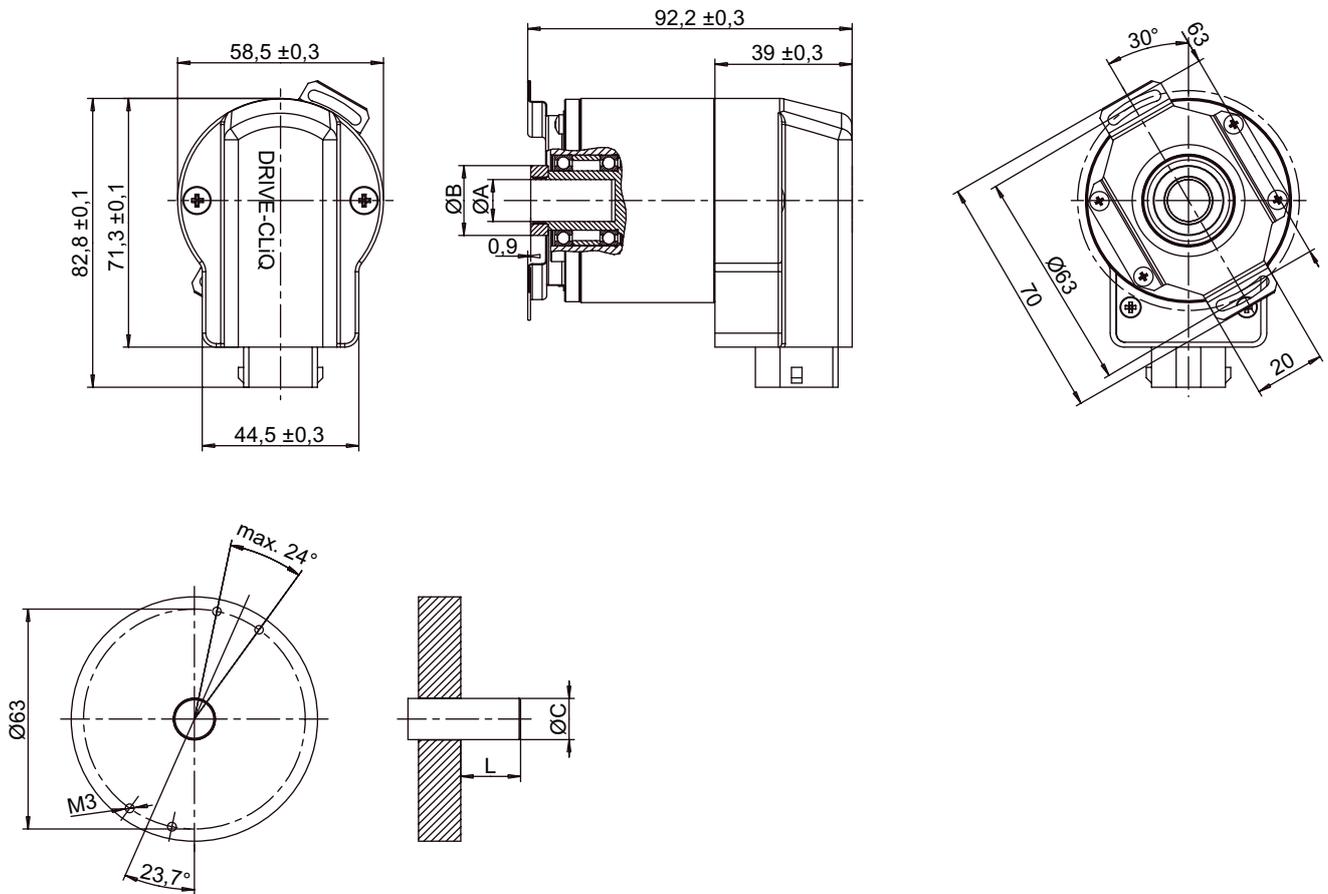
Maßzeichnung: Sack-Hohlwelle
